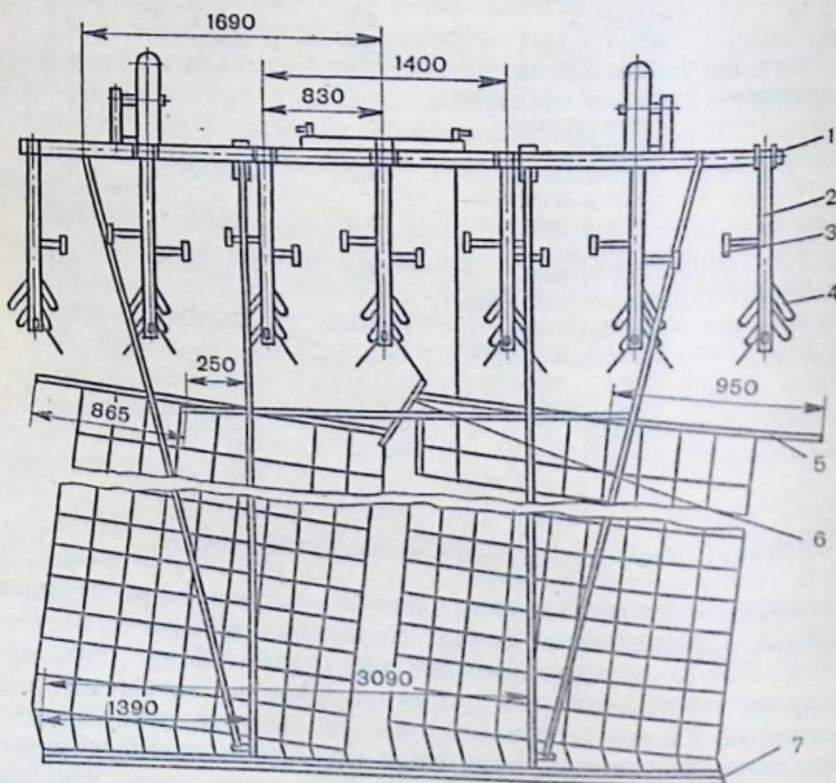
Культиватор КРН-4,2Г в агрегате с сетчатой бороней (вид сверху):
